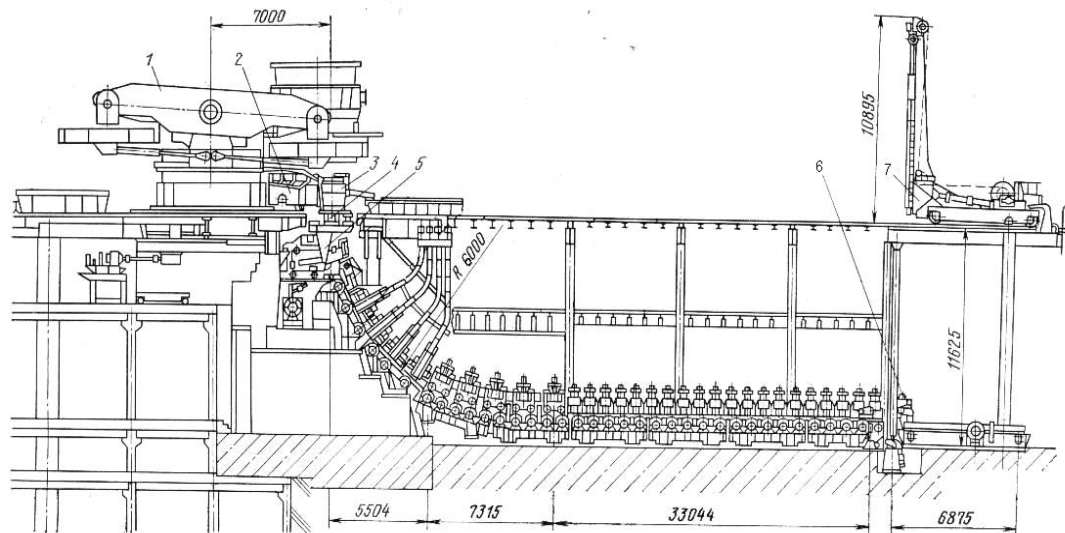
Криволинейная машина непрерывного литья заготовок: 1 – разливочный стенд; 2 – тележка промковша; 3 – промежуточный ковш; 4 – кристаллизатор; 5 – механизм качания ; 6 – затравки; 7 – машина для ввода затравки
